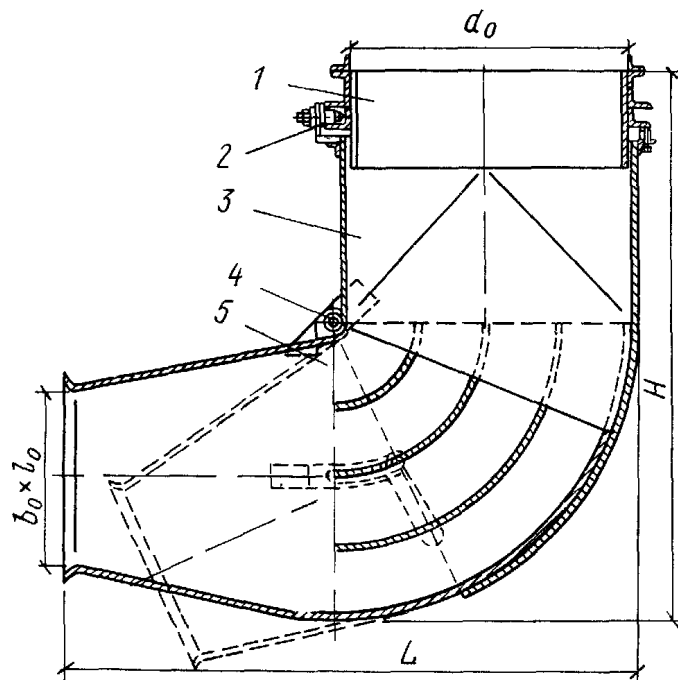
Поворотный душирующий патрубок типа ППД
